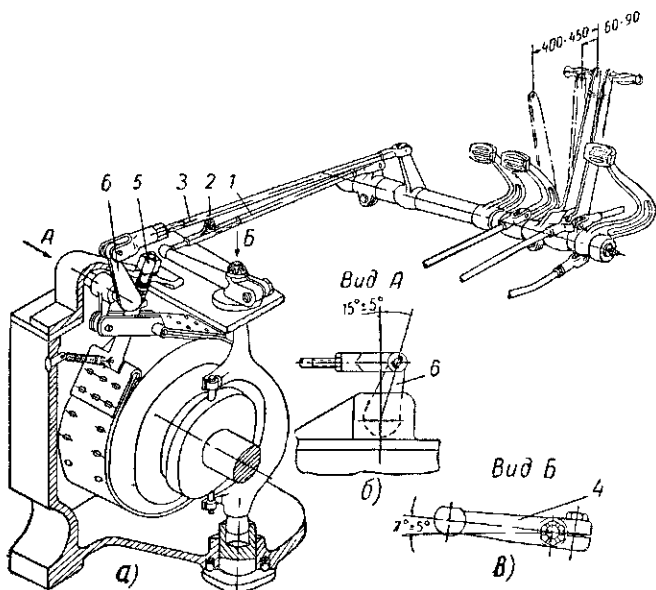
Схема регулировки рычагов тормозов и муфт поворота:
